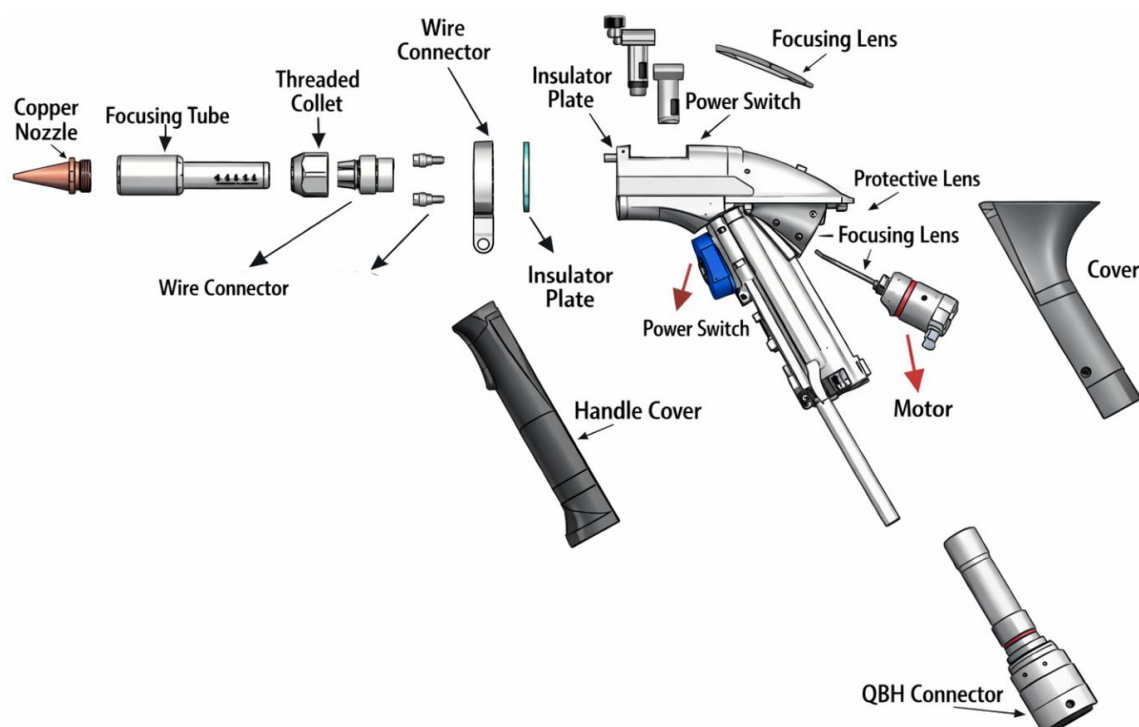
Diagrama de la antorcha de soldadura láser manual
